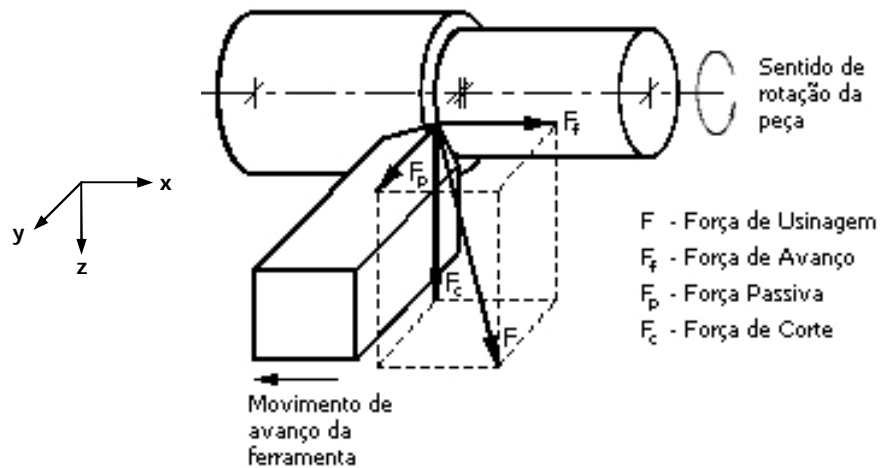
Componentes ortogonais da força de usinagem no torneamento [11; 31; 75; 76; 138; 139]
